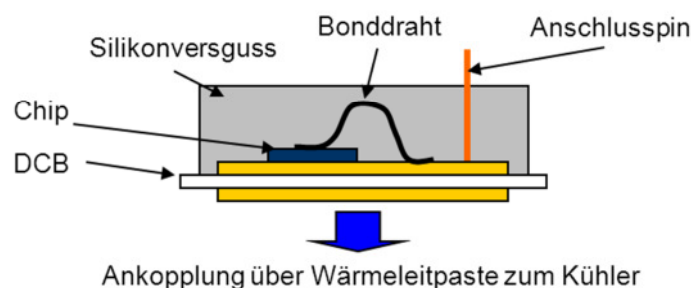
Aufbautechnik Pinmodul (Prinzipskizze)
